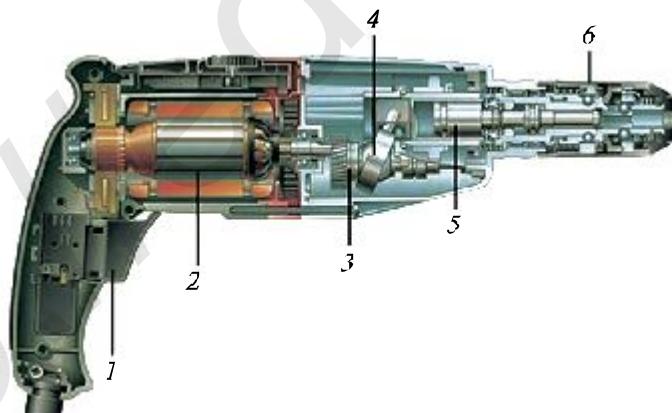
Строение перфоратора: 1 – кнопка включения; 2 – двигатель; 3 – муфта безопасности; 4 – двигающийся подшипник; 5 – ротационный качающийся механизм; 6 – шатрон типа SDS
